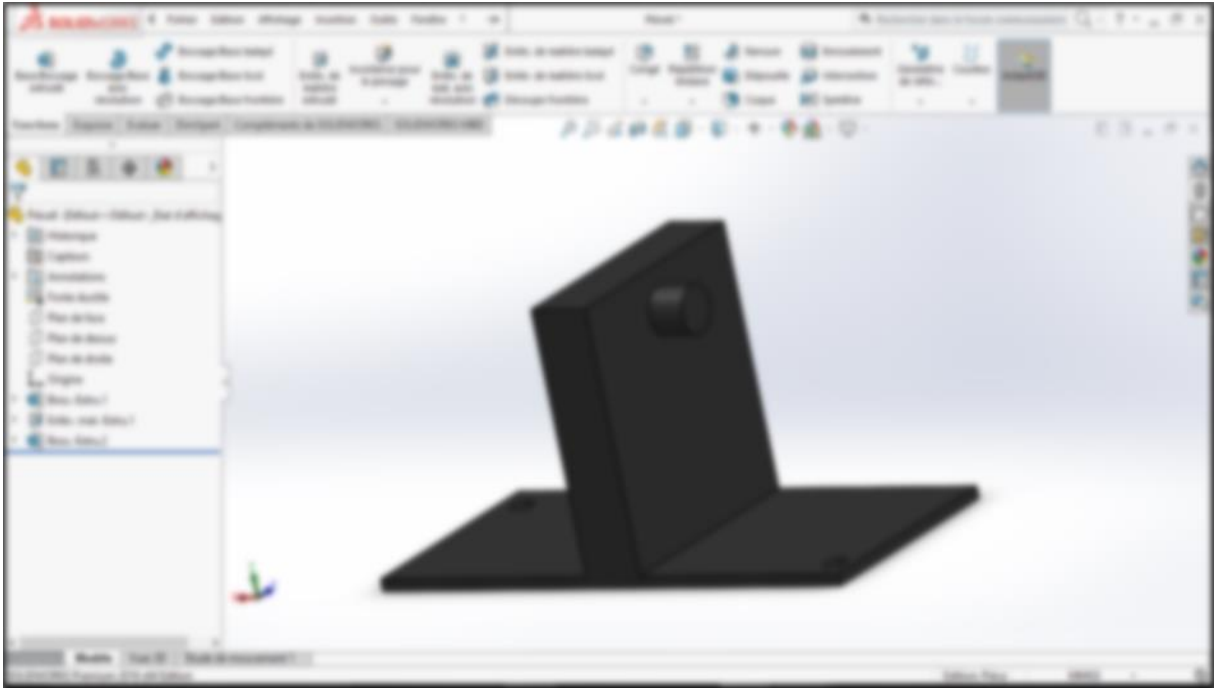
Support de forme (T) en 3D sous-SolidWorks.
